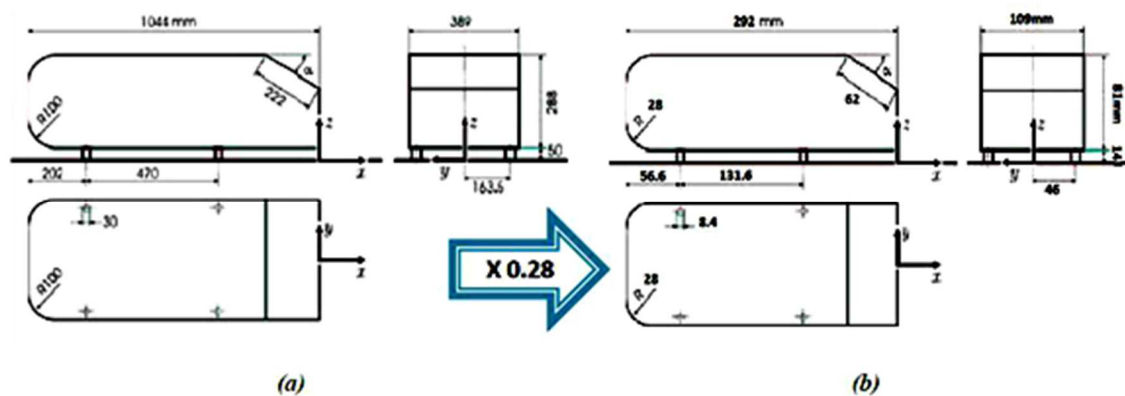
Dessin de définition ((a) : dimensions d'Ahmed et al (b) : dimension de notre maquette).
